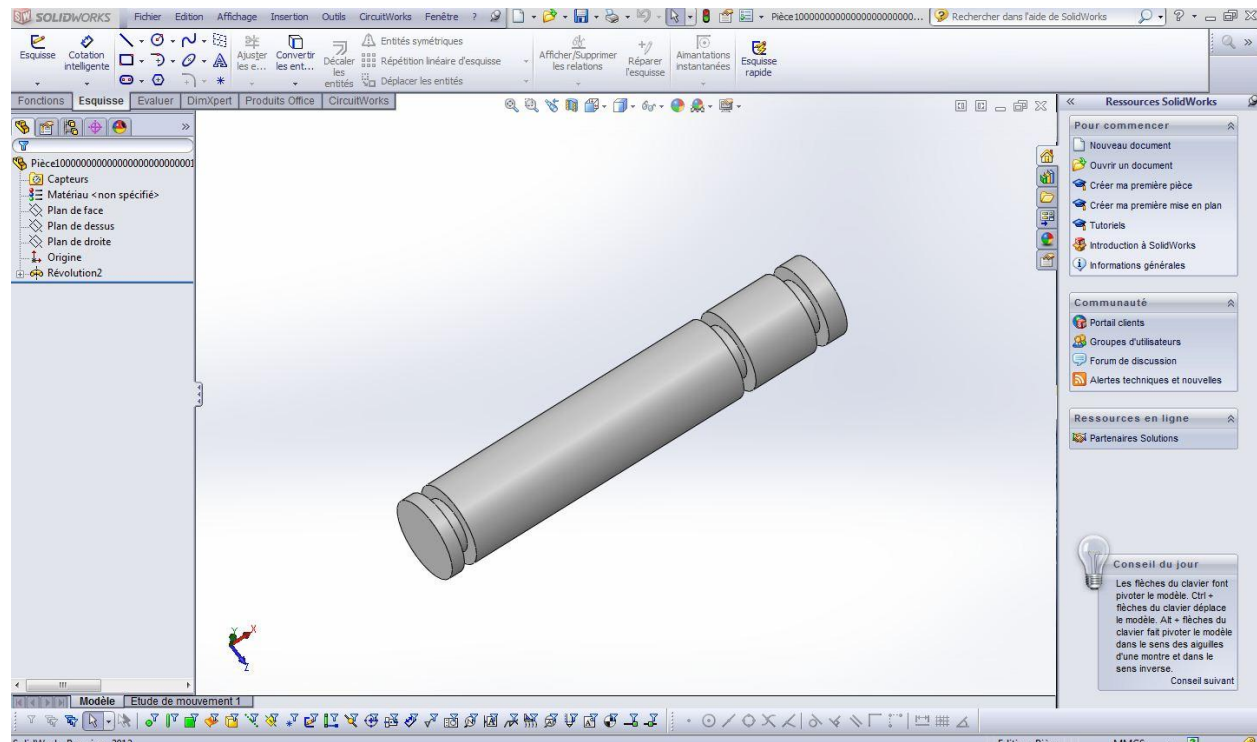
Vue Goupille cannelée réalisée sous SOLIDWORKS
